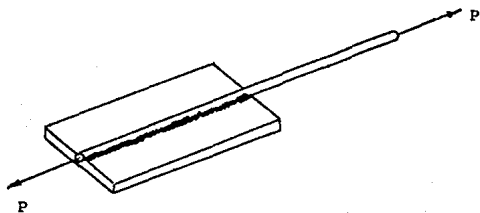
Tipos de conexión soldada a tensión.
